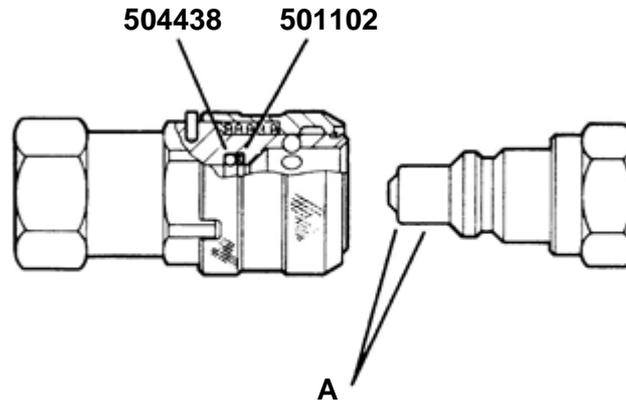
Kupplungen Buchsen 110439 und Stecker 110438
